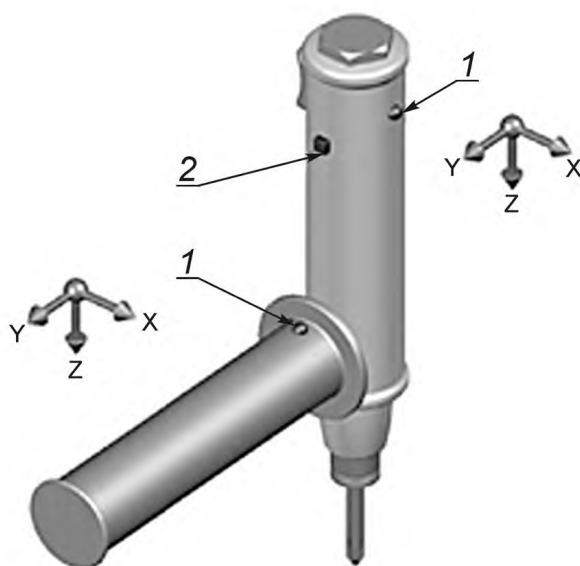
Точки и направления измерений для трещоточного гайковерта
